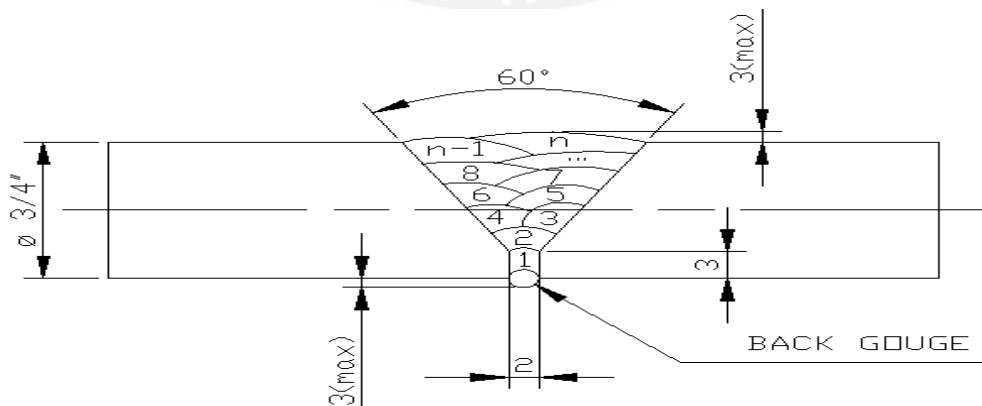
Detalle geométrico de la junta soldada de barra de 5/8".
